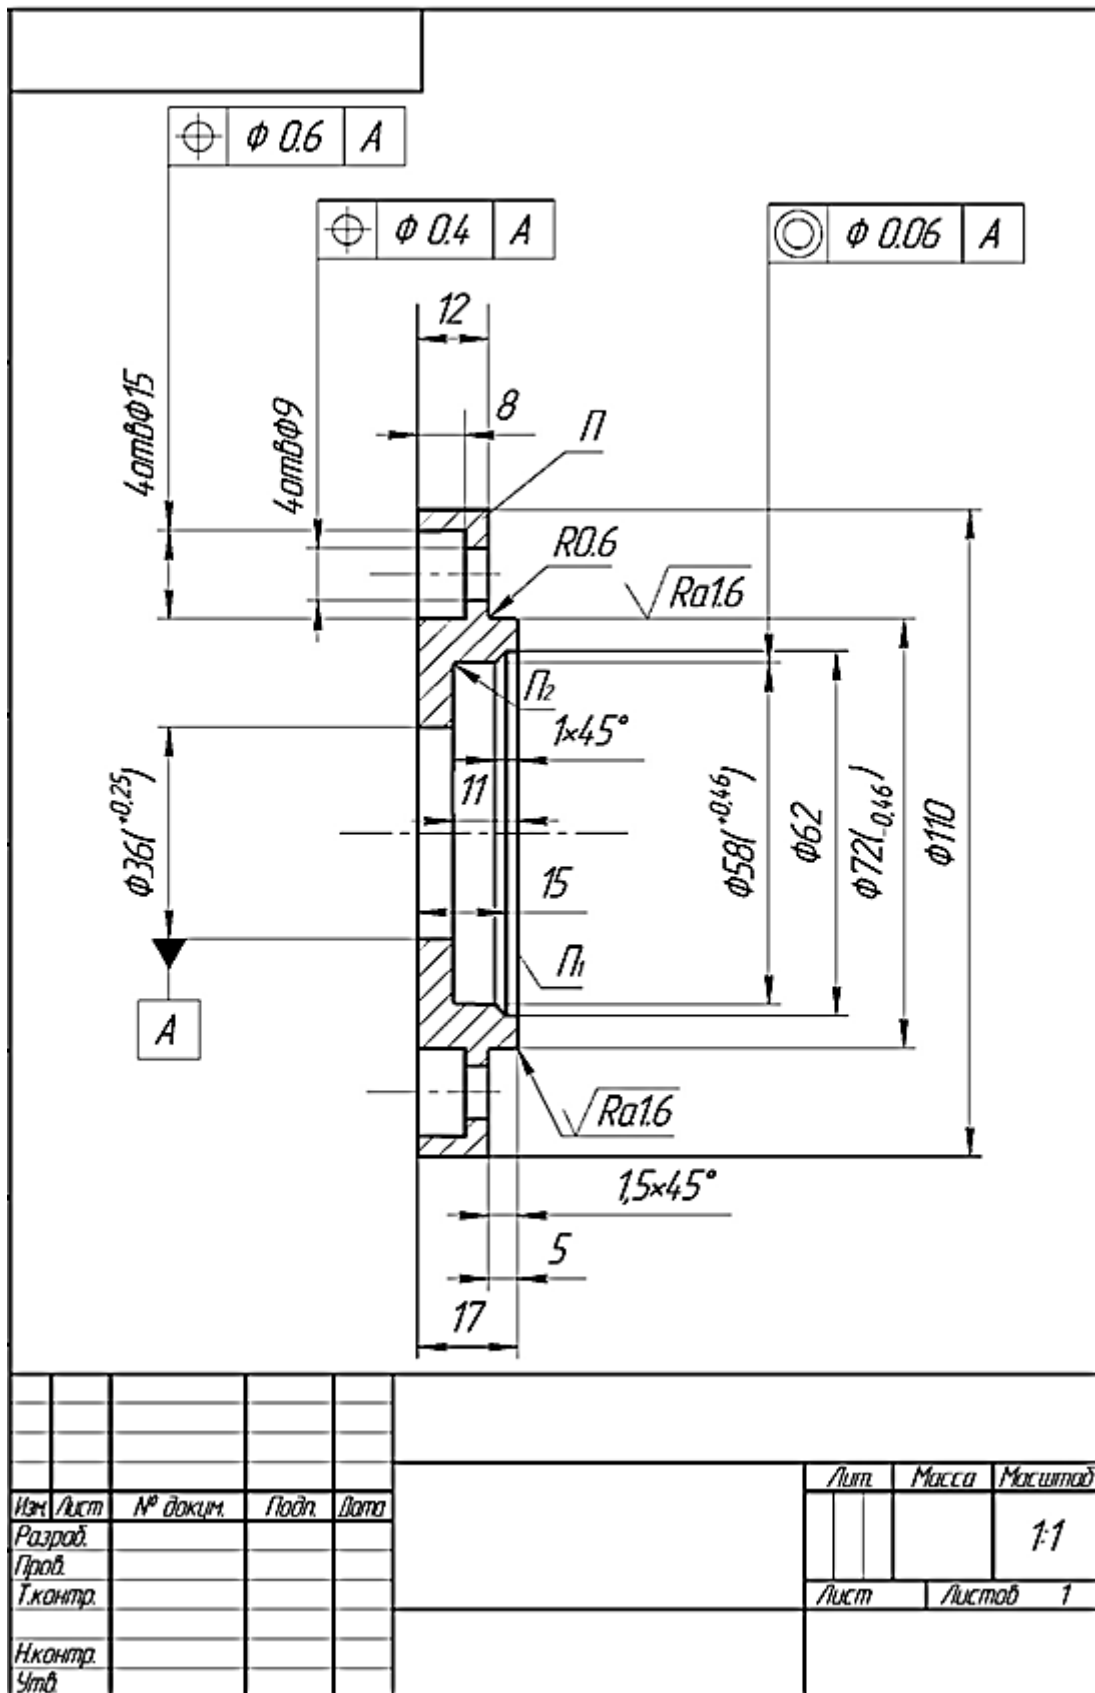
Рабочий чертеж крышки подшипника (правильный)
